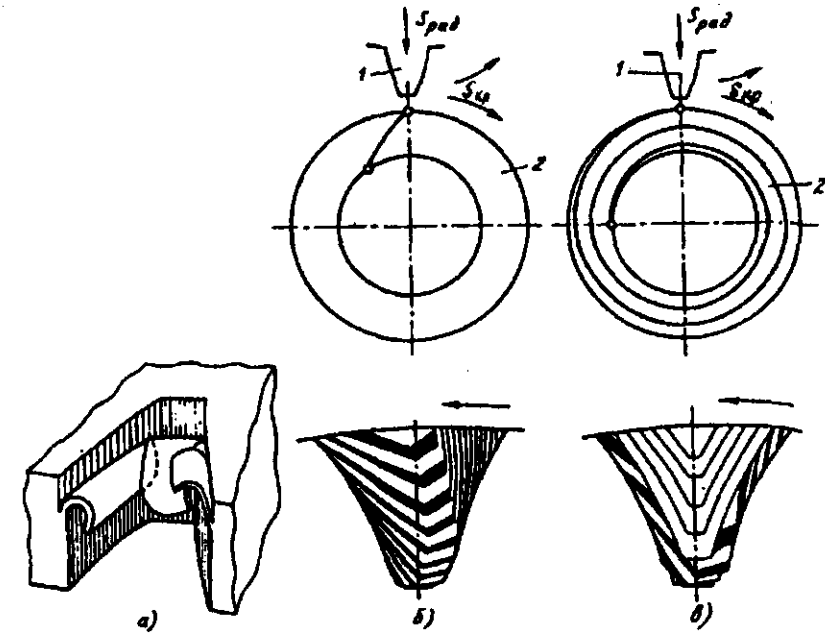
Форма стружки и схемы зубодолбления: а – трехкомпонентная стружка; б – радиальное движение подачи; в – спиральный метод с постоянным движением подачи; 1 – инструмент; 2 – заготовка
